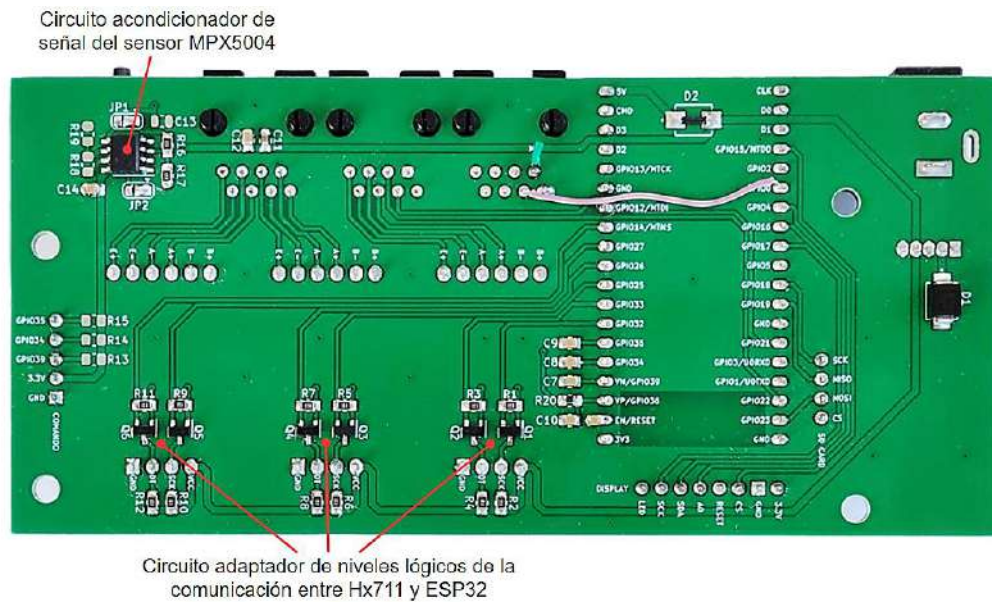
Cara posterior de la placa PCB con componentes soldados.
